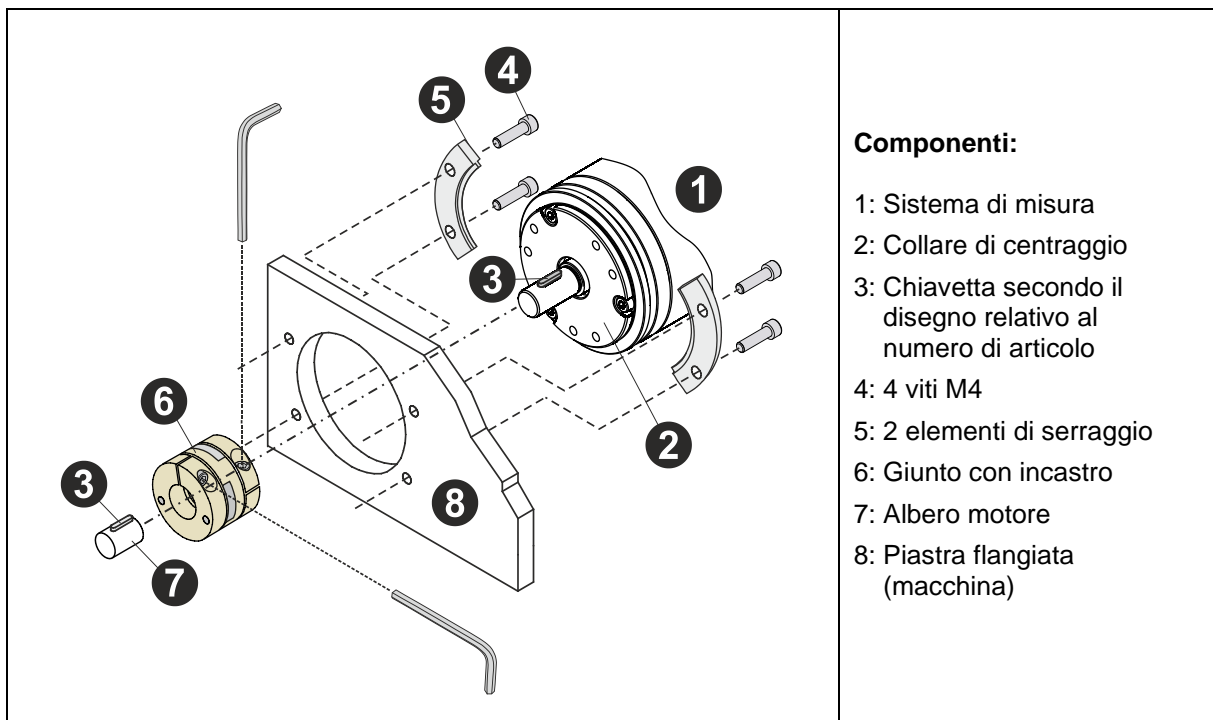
Installazione con elementi di serraggio, rappresentazione schematica
